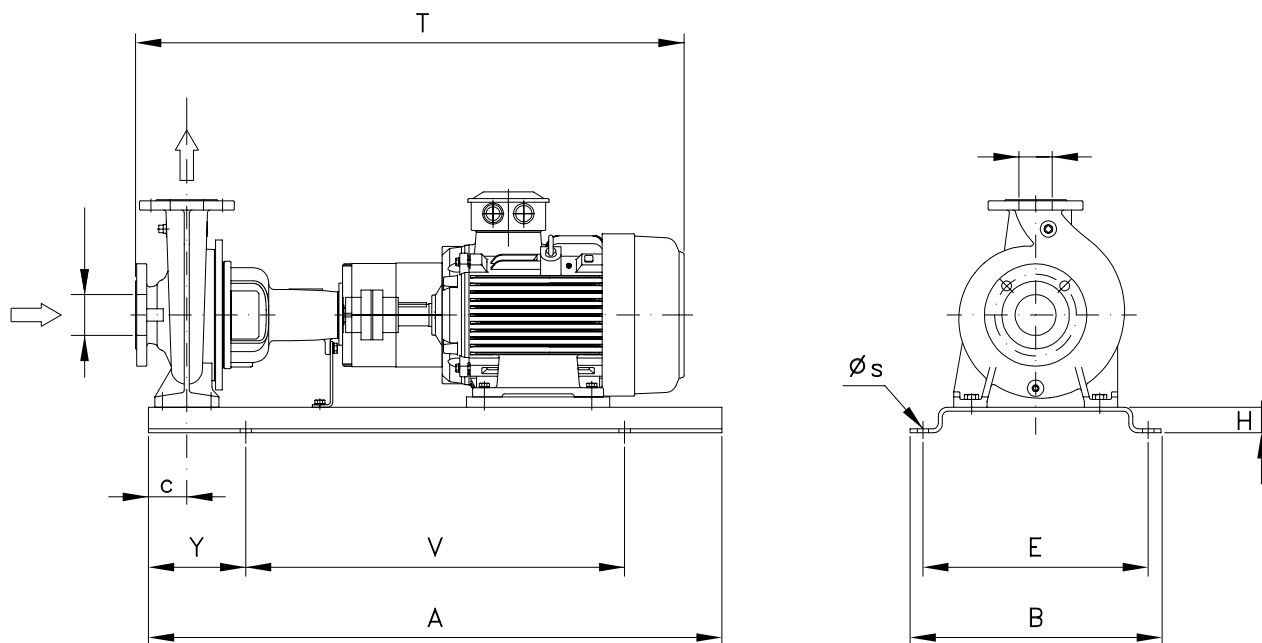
SEMELLE FABRIQUÉE - ÉGALE ET SUPÉRIEURE À 110 kW
